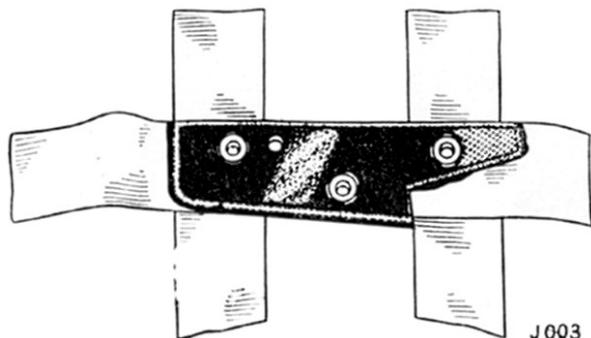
Position de la bande adhésive sur les joints en caoutchouc
